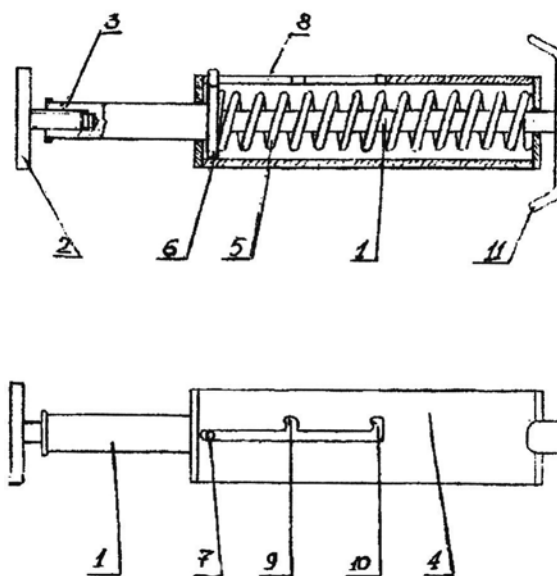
Общий вид устройства для воспроизведения политравмы: 1 – металлическая штанга; 2 – съемный ударник; 3 – метрическая резьба; 4 – цилиндр; 5 – тарированная пружина; 6 – ограничитель; 7 – фиксатор; 8 – продольный паз; 9, 10 – выемки; 11 – ручка-скоба
